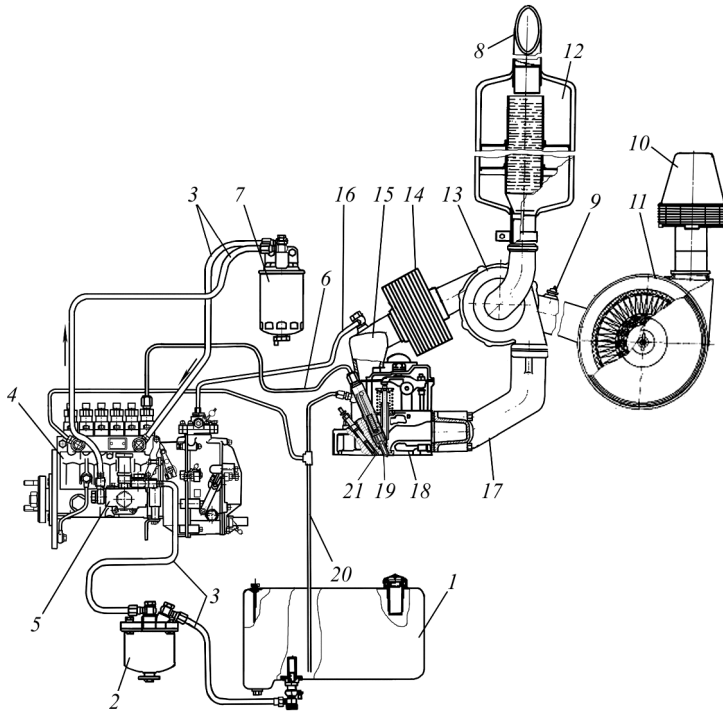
Схема системы питания дизельного двигателя Д-260S2: 1 – топливный бак; 2 – фильтр грубой очистки топлива; 3 – трубки топливные низкого давления; 4 – топливный насос высокого давления; 5 – топливоподкачивающий насос; 6 – трубка топливная высокого давления; 7 – фильтр тонкой очистки топлива; 8 – выхлопная труба; 9 – датчик засоренности воздушного фильтра; 10 – моноциклон; 11 – воздухоочиститель; 12 – глушитель; 13 – турбокомпрессор; 14 – охладитель наддувочного воздуха; 15 – коллектор впускной; 16 – трубка пневмокорректора; 17 – коллектор выпускной; 18 – головка цилиндров; 19 – форсунка; 20 – трубка отвода топлива в бак; 21 – свеча накаливания
